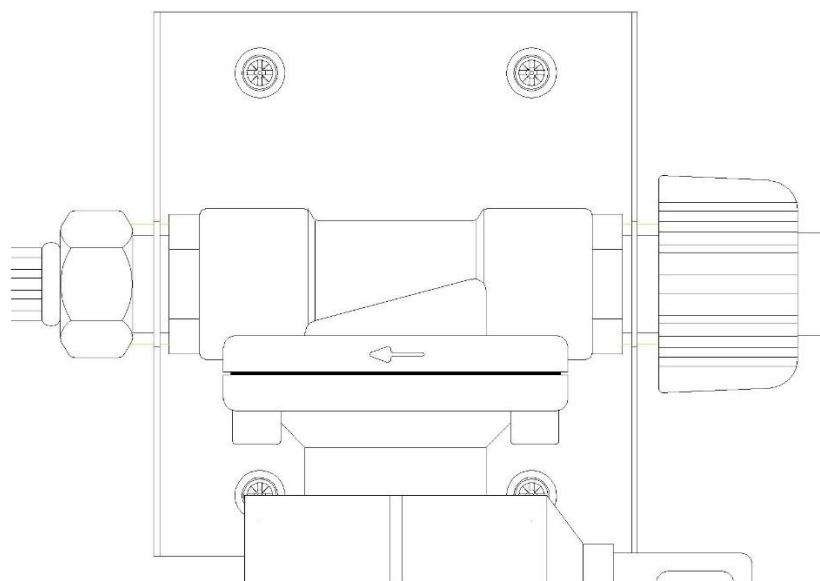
Collegamento elettrovalvola alla sistema di fissaggio
